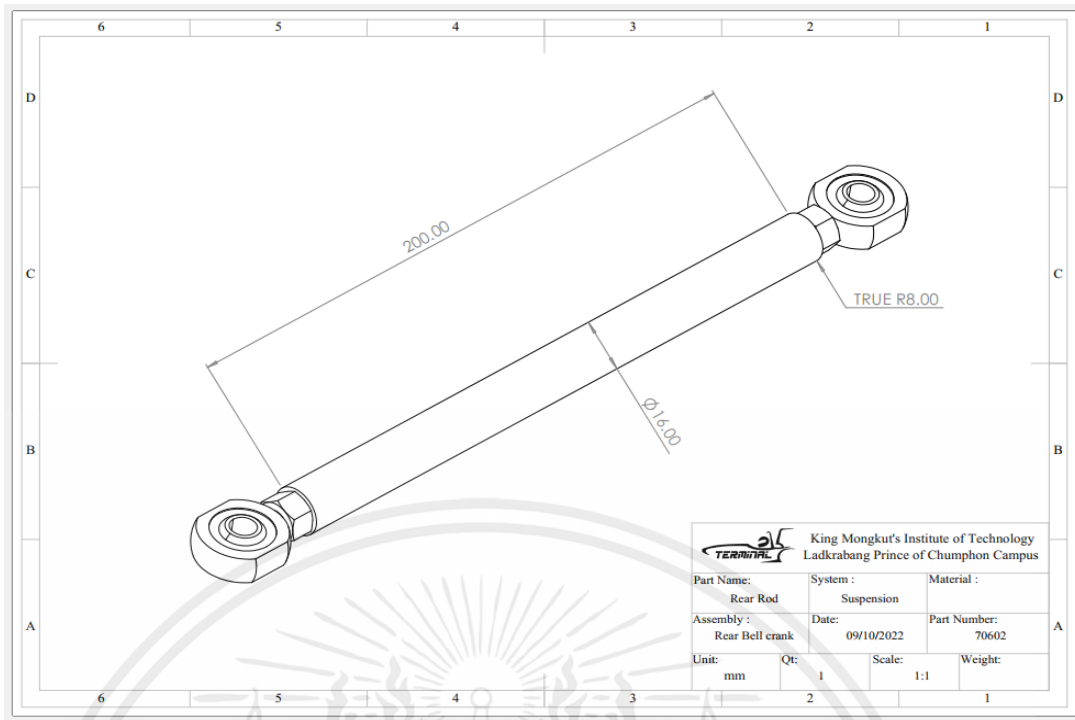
ส่วนประกอบของชุดกระเดื่อง ด้านหลัง (Rear Bell Crank Assembly)
